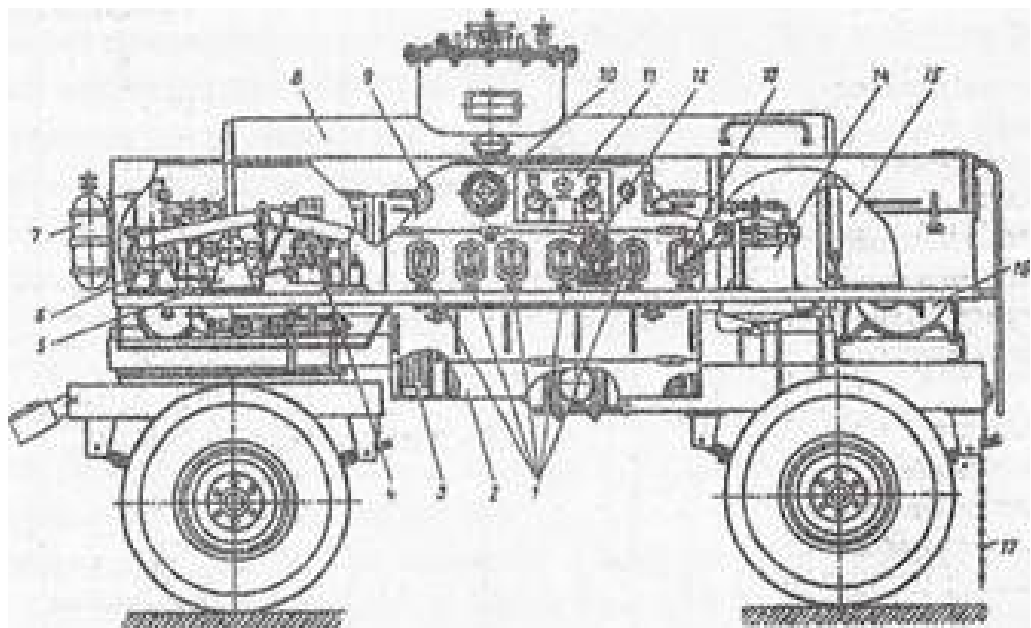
Механізований заправний агрегат МЗ-3905Т (ОЗ — 1401): 1 — роздавальні крани; 2 — кожух барабанів; 3 — барабан з раздаточним рукавом; 4 — компресор; 5 — привід агрегату; 6 — насос для дизельного палива; 7 — вогнегасник; 8 — цистерна для дизельного палива; 9 — лічильник дизельного палива; 10 — лічильник дизельної олії; 11 — шитий управління; 12 — кран розподілу стислого повітря; 13 — пістолет-нагнітач пневматичного солідолонагнітача; 14 — бункер пневматичного солідолонагнітача; 15 — місткість для трансмісійної масла; 16 — місткість для води; 17 — заземлення
